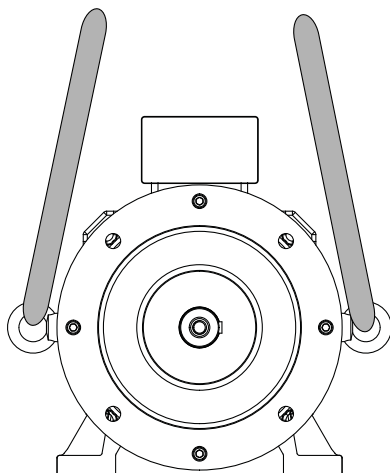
Транспортировка двигателя с двумя рым-болтами по бокам корпуса двигателя
